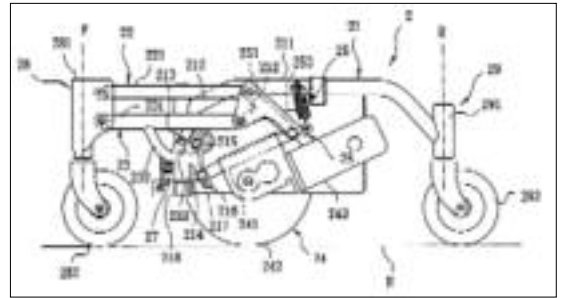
Radaufhängung am Mittelachsenantrieb, Patentzeichnung EP 1 832 266.
